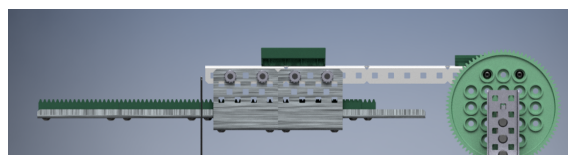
VEX EDR - Detail pohybového ústrojí
